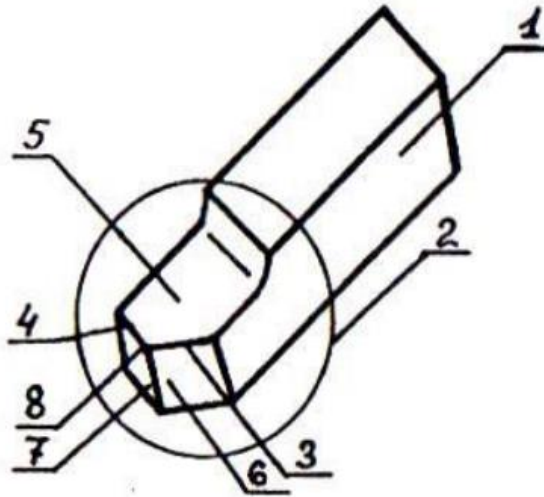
Елементи різця: 1 - стрижень (тіло) різця; 2 – головка різця; 3 - головна ріжуча кромка (лезо); 4 - допоміжна ріжуча кромка; 5 – передня поверхня; 6 – головна задня поверхня; 7 – допоміжна задня поверхня; 8 – вершина різця.
